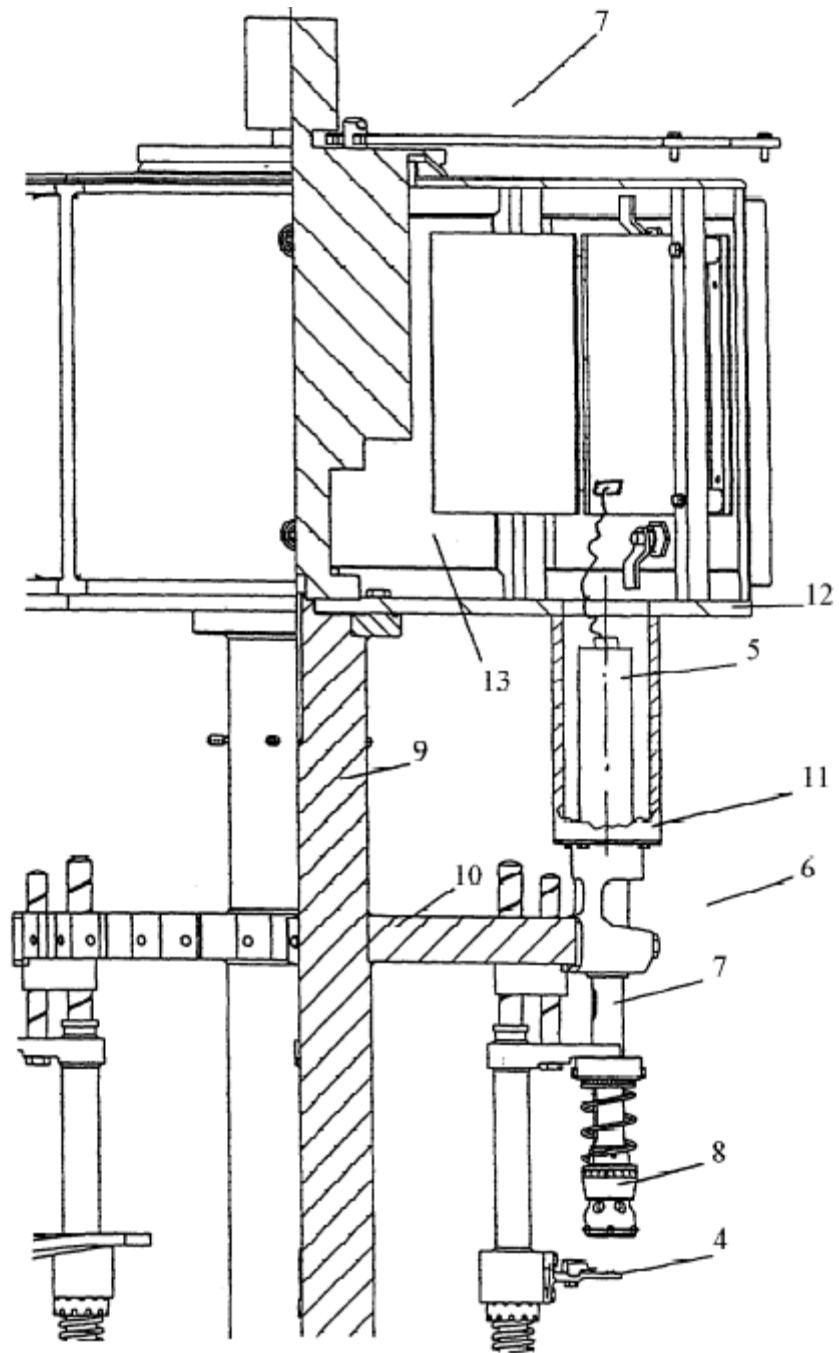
Схема закупорювальної машини для закривання пляшок
